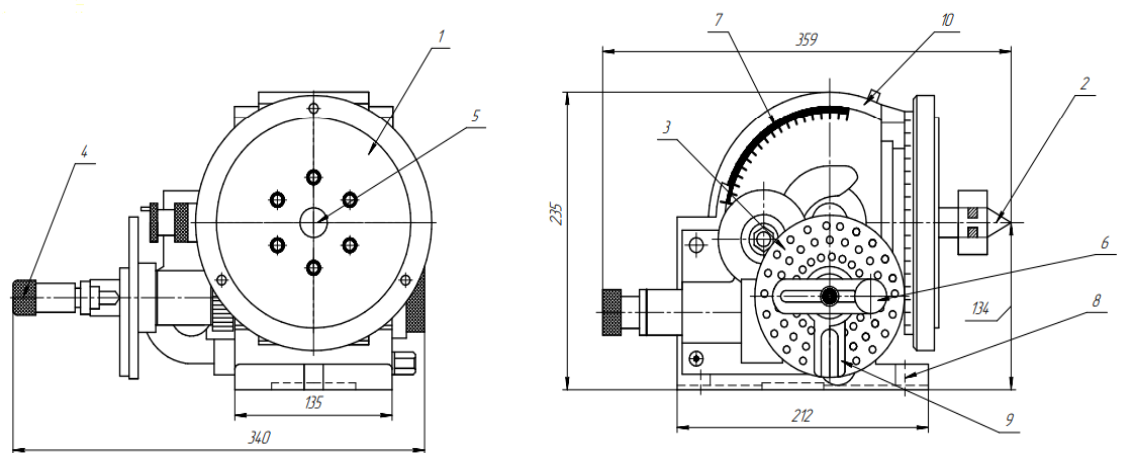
Ділильна головка для верстатів з ЧПК
